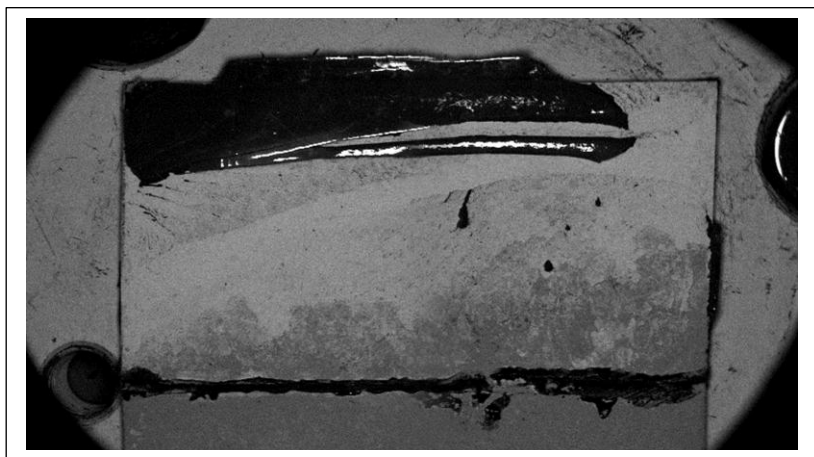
e 123 - Apresentam superfícies de fratura, as setas indicam o caminho do processo corrosivo em direção ao centro da região adesivada. Adesivo Puro. FONTE LAB. FIAT
